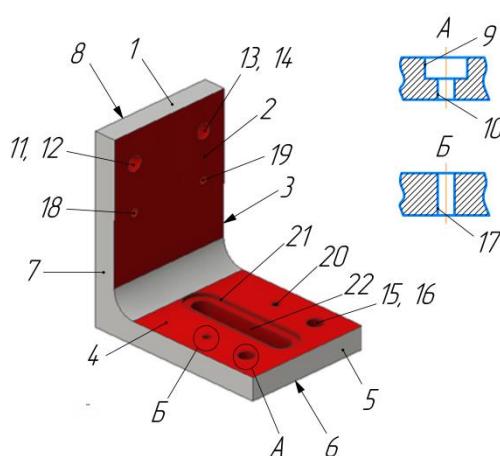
Класифікація поверхонь оброблюваної деталі
